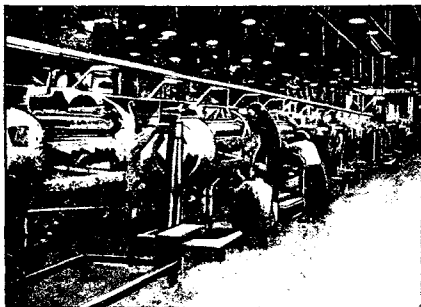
Стационарное приспособление для сборки хвостовой части фюзеляжа
